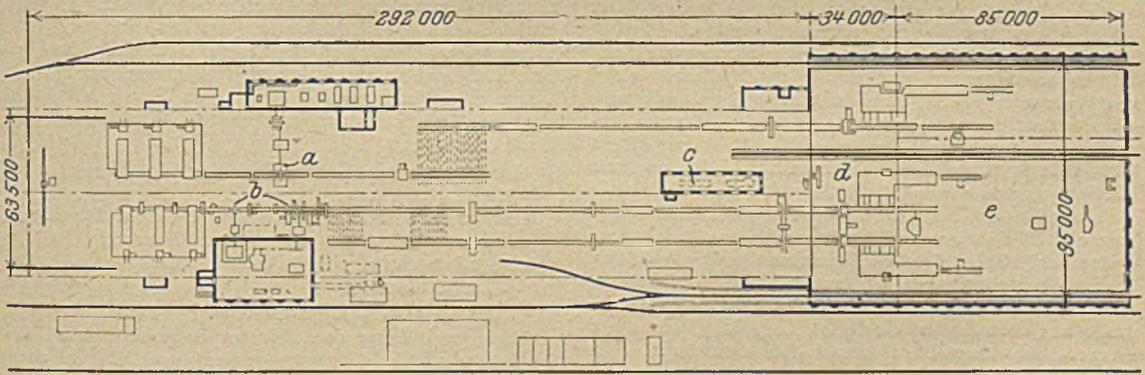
Lageplan des Blechwalzwerkes der Brier Hill Steel Co., Youngstown.
